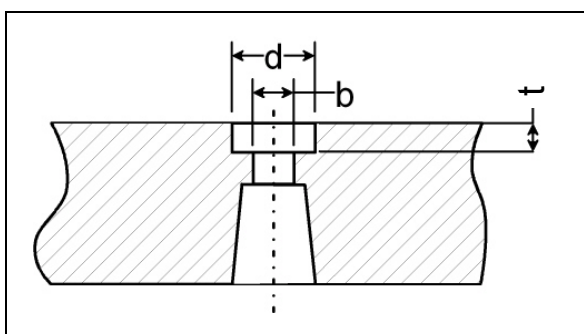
Konstruktion zur Ausführung einer Vorkammer nach Wei92
